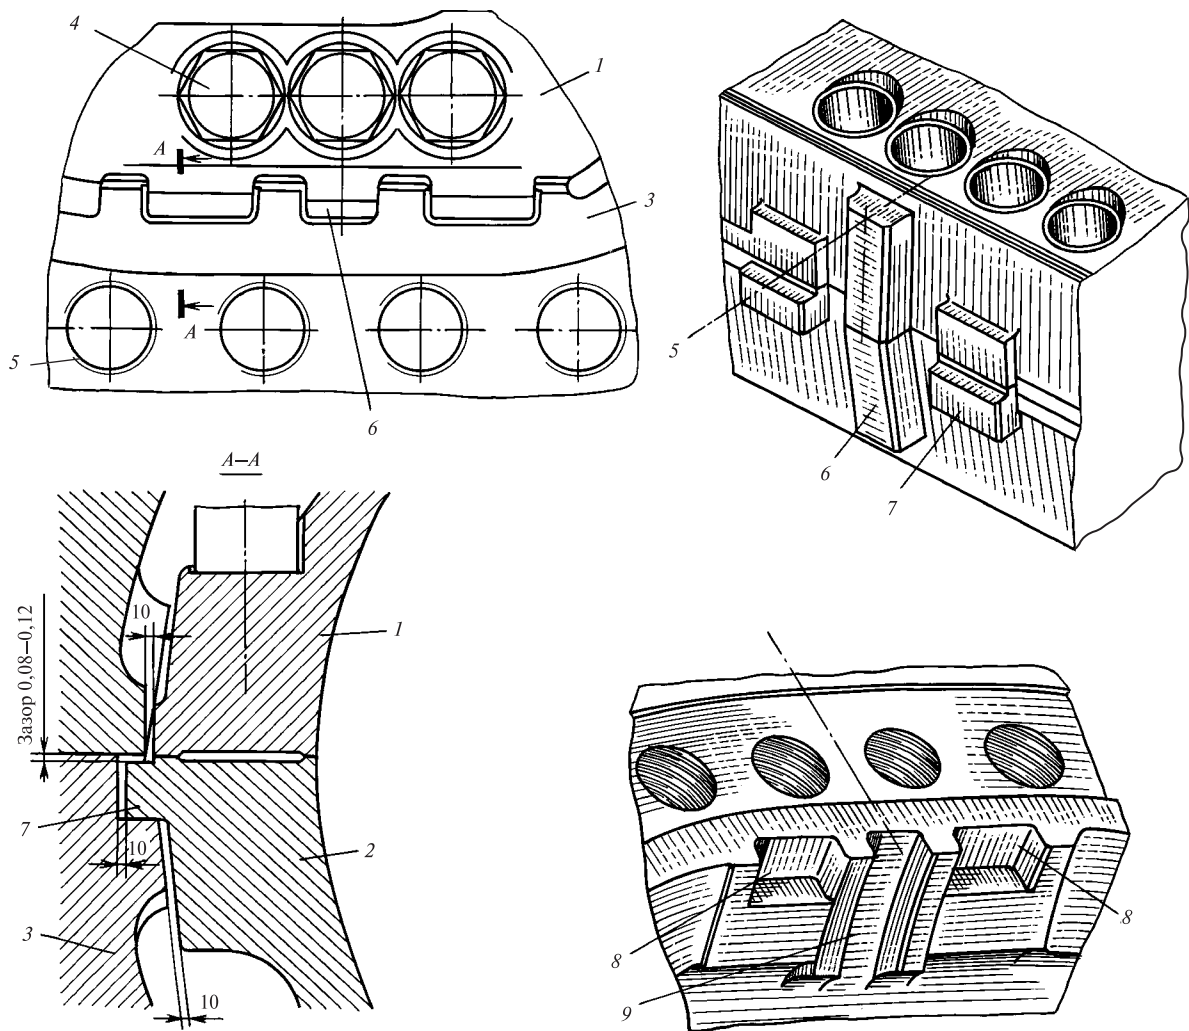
Детали подвески внутреннего корпуса двухстенного ЦВД во внешнем корпусе:
